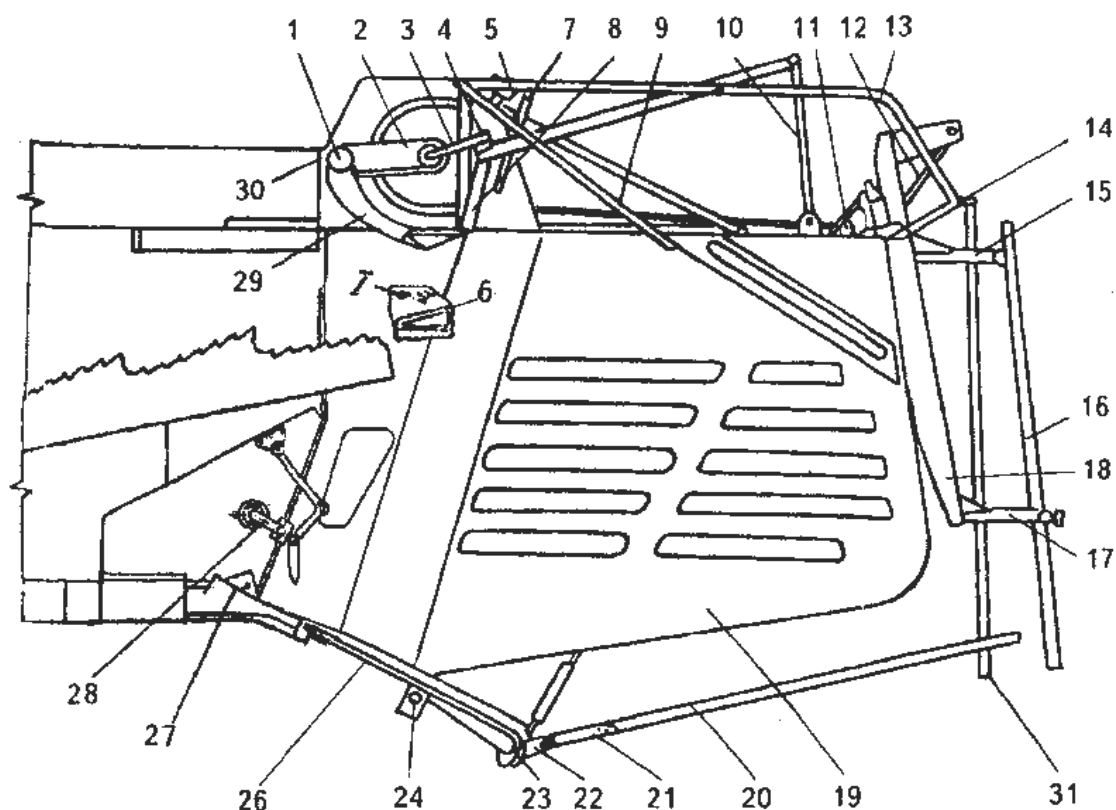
Копнитель навесной гидрофицированный (продольный разрез): 1 – балка рамы; 2 – кронштейн соломонабивателя; 3 – соломонабиватель; 4 – подшипник; 5 – датчик; 6 – щиток сброса соломы; 7 – стеблесъемник; 8 – граблины; 9 – сигнализатор; 10 – кулиса; 11 – гидроцилиндр; 12 – тяга; 13 – уголок верхней решетки камеры; 14 – поперечный угольник; 15 – верхний брус клапана; 16 – клапан; 17 – нижний брус клапана; 18 – рычаг клапана; 19 – боковина; 20 – палец; 21 – звено промежуточное; 22 – кронштейн; 23 – брус задний; 24 – брус передний подвески дна; 25 – окно боковины; 26 – днище; 27 – лоток; 28 – половонабиватель; 29 – отсекатель; 30 – капот; 31 – сигнализатор сброса копны; I – канал подпрессовки
